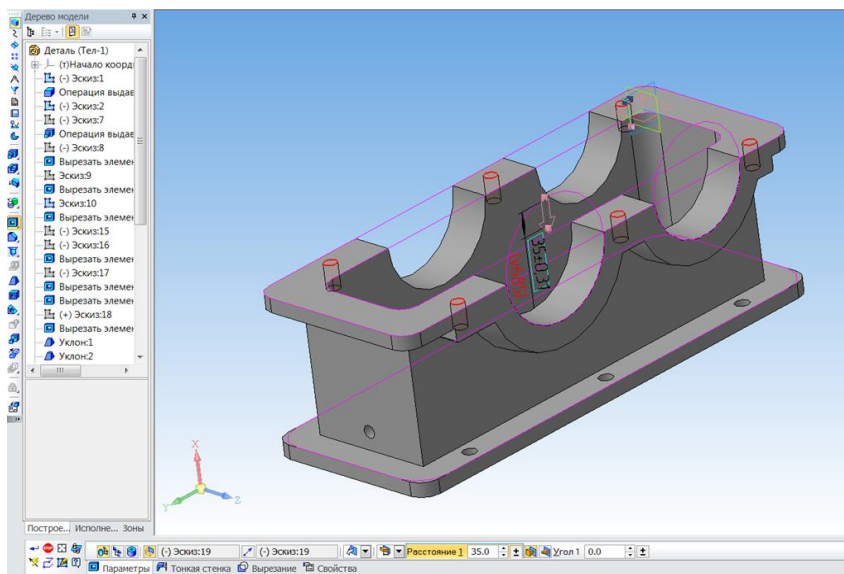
Снимок экрана при разработке корпуса редуктора
